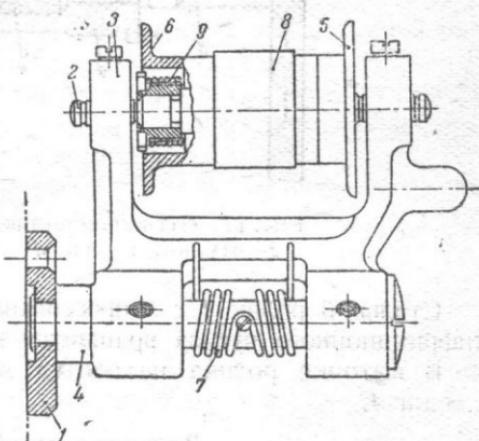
Прижимной ролик: 1—фланец; 2—центры; 3—корпус; 4—ось; 5—наружная щечка; 6—задняя щечка; 7—пружина; 8—ролик; 9—пружина
